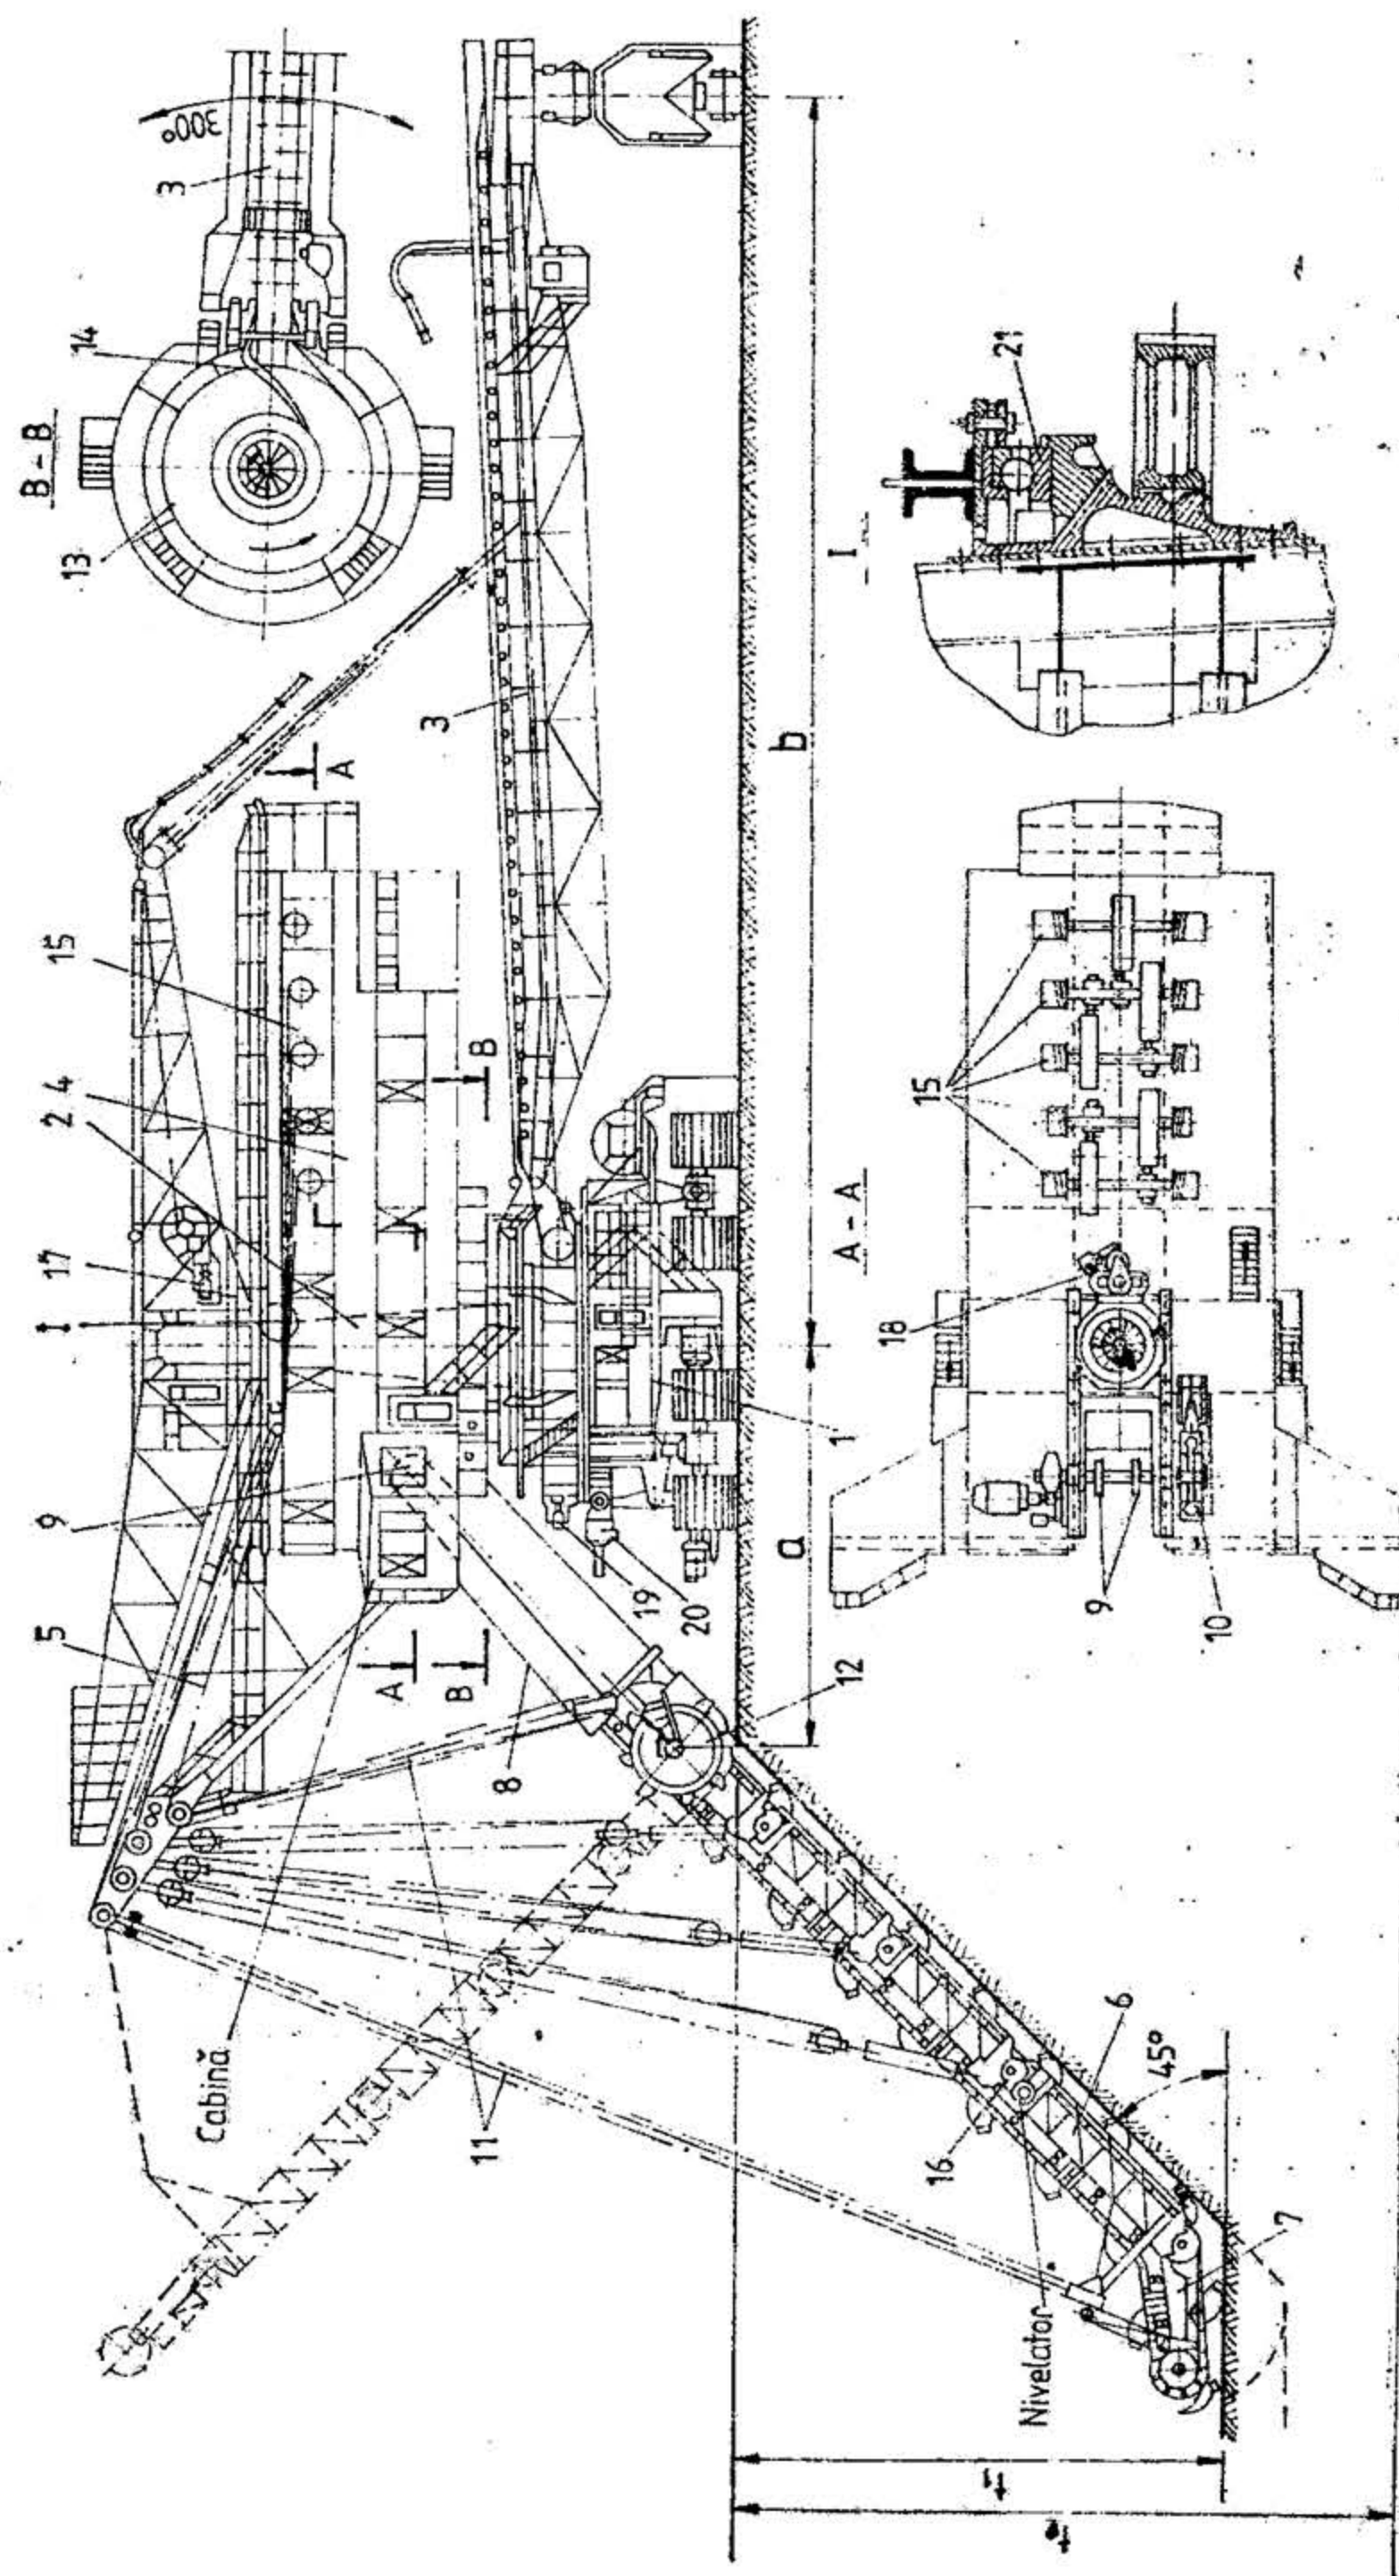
Schema constructivă a excavatorului elindă ERS-580 pe șenile de construcție R.D.G.:
